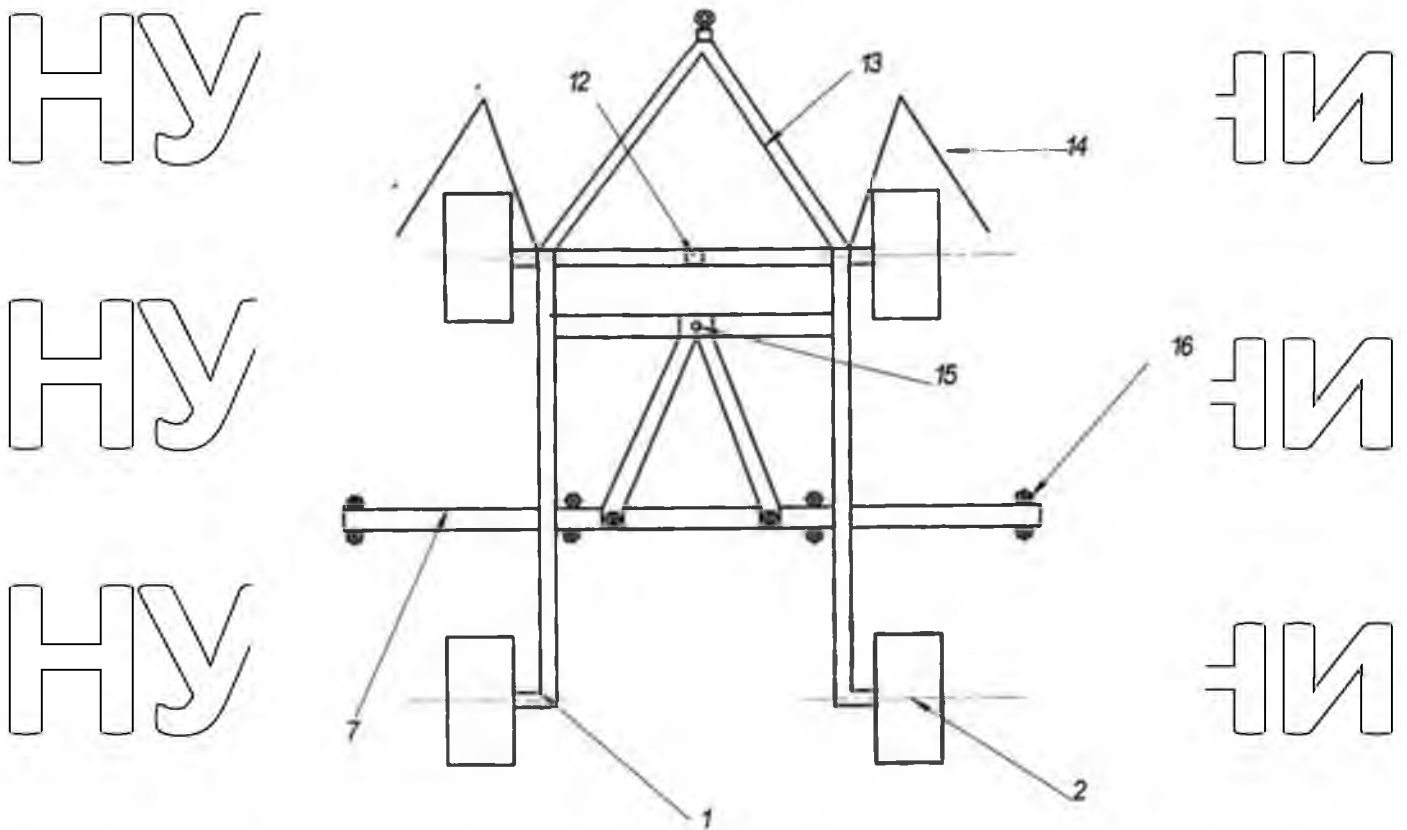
Положення робочих органів і основних елементів макетної лабораторно-польової установки (вид зверху): 1-рама; 2-колеса; 7-ряділь; 12-поворотний шарнір; 13-сшиця; 14-грудковідбивачі; 15-рукомятка; 16-гайки кріплення хомутів.
